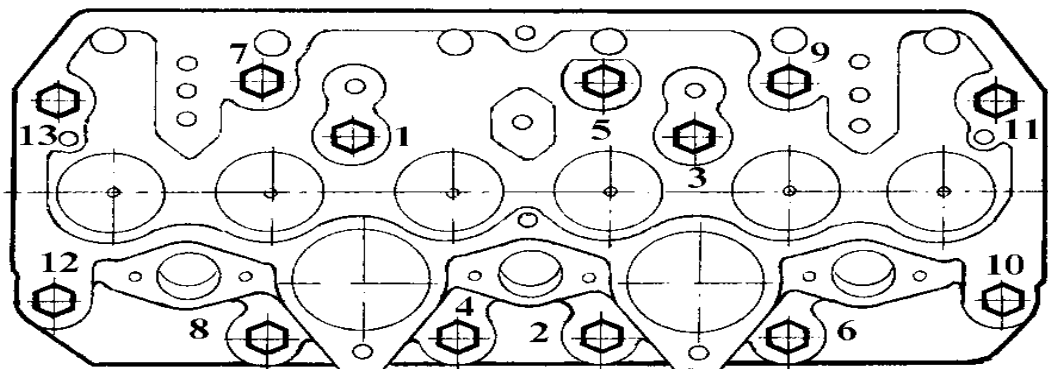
Схема последовательности затяжки болтов крепления головки цилиндров
